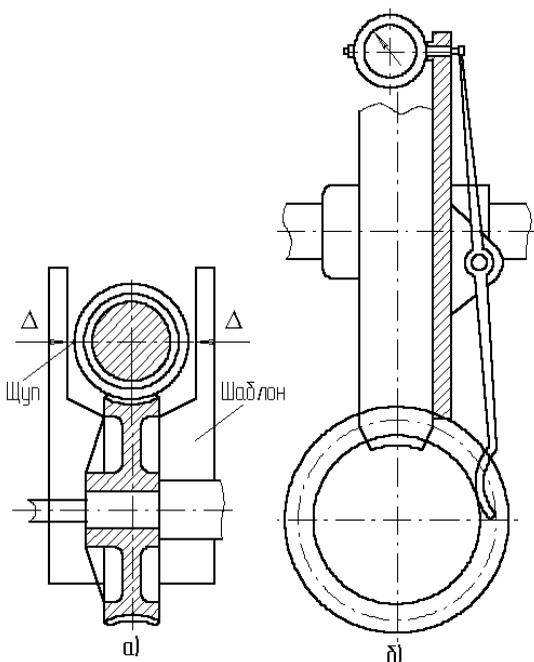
Схемы контроля положения червяка относительно червячного колеса: *а)* с помощью щупа; *б)* с помощью индикаторного приспособления
